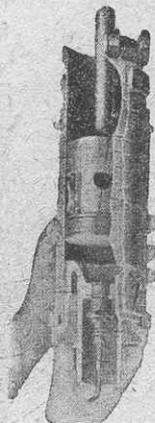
Золотник и головка цилиндра двигателя Виллис-Найт.
